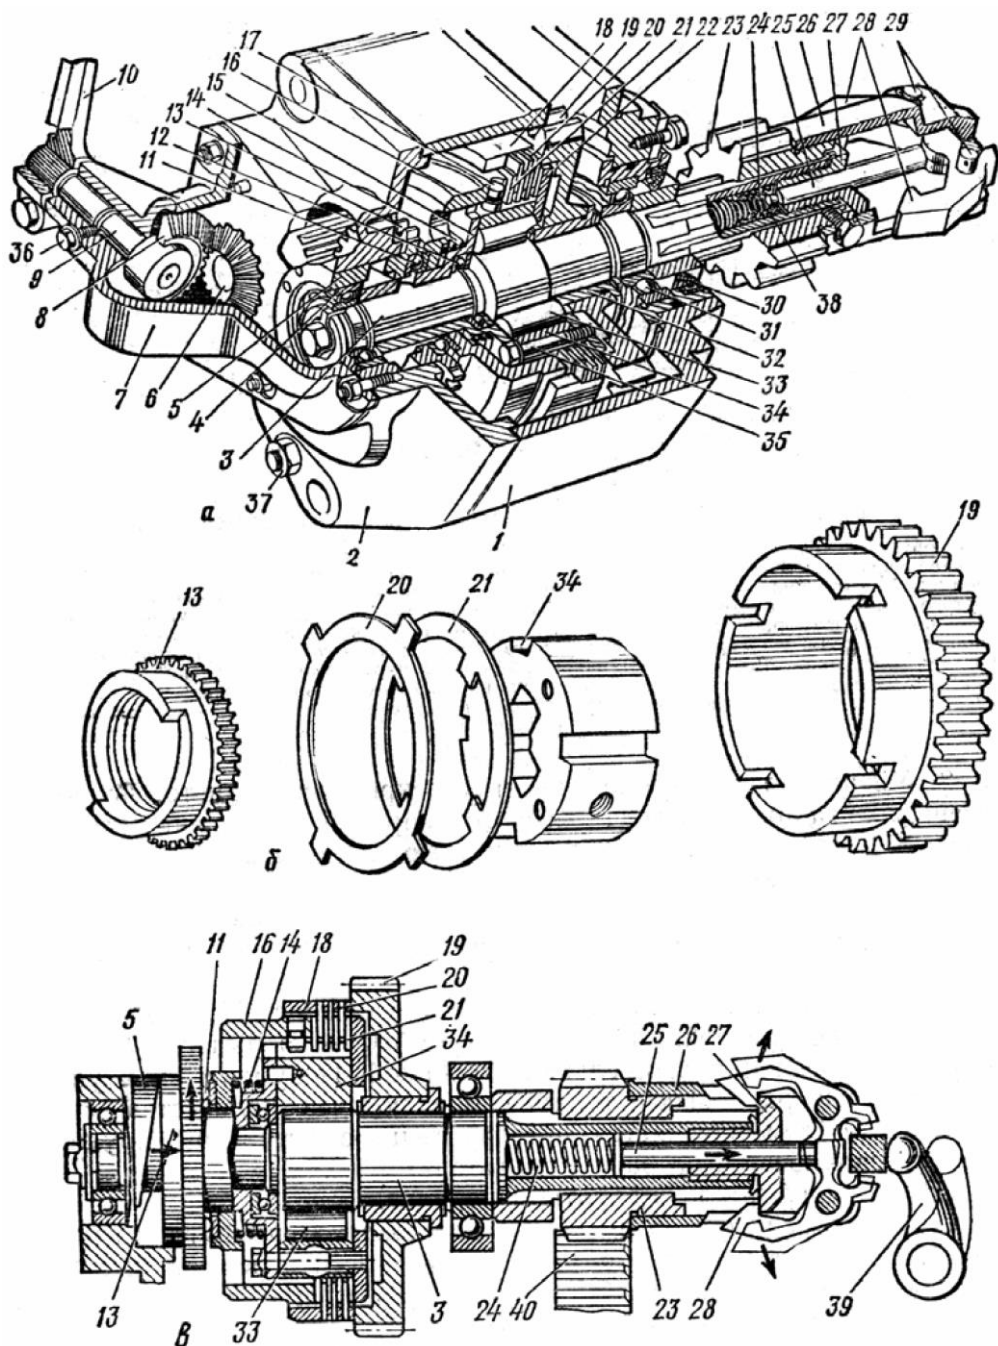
Механизмы передачи системы пуска: а - редукторная часть в сборе; б - детали сцепления; в - обгонная муфта; 1 - корпус; 2 - крышка; 3 - вал; 4, 11, 12 и 31 - подшипники; 5 - неподвижный упор; 6 - коническая шестерня; 7 - крышка механизма включения; 8 - сектор; 9 - валик; 10 - рычаг; 13 - подвижный упор; 14, 24 и 33 - пружины; 15 - ступица обгонной муфты; 16 - нажимной диск; 17 - штифт; 18 - ведущий барабан; 19 - шестерня редуктора; 20 и 21 - ведущие и ведомые диски; 22 - упорный диск; 23 - шестерня автомата выключения; 25 - толкатель; 26 - держатель; 27 - направляющая втулка; 28 - груз-защелка; 29 - ось груза; 30 - манжета; 32 - втулка; 33 - ролик; 34 - обойма обгонной муфты; 35 - стяжной болт; 36 - фиксирующий болт; 31 - гайка; 39 - рычаг включения автомата; 40 - венец маховика
